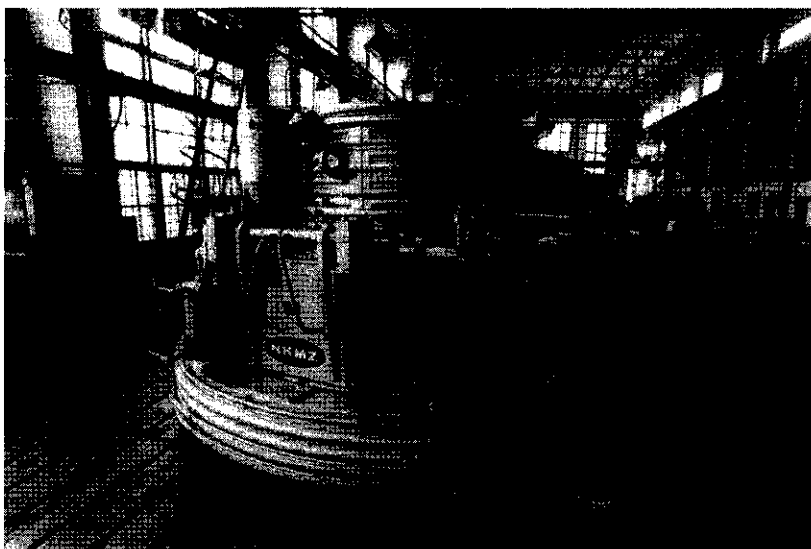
Крышка ковша-печи конструкции НКМЗ
